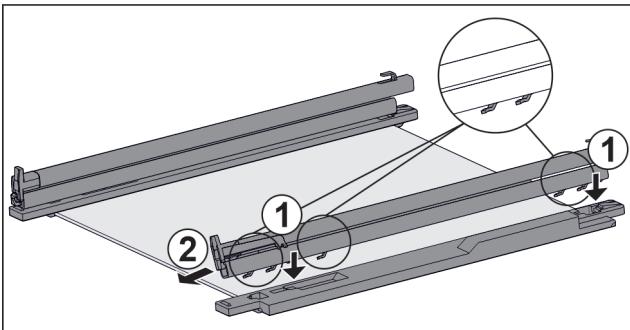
Скляна пластина з рейками та деталями для підтримки
